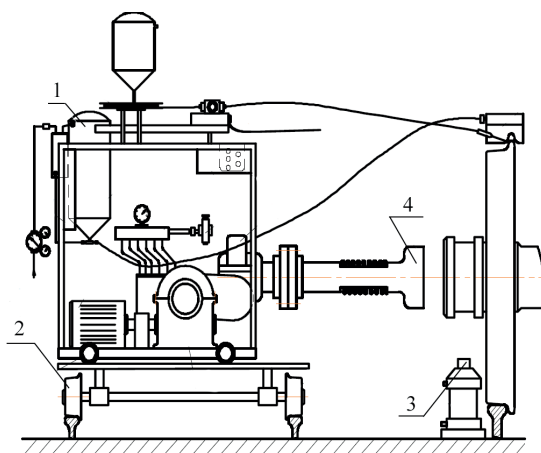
Схема установки для наплавки гребней колесной пары без выкатки [1]
